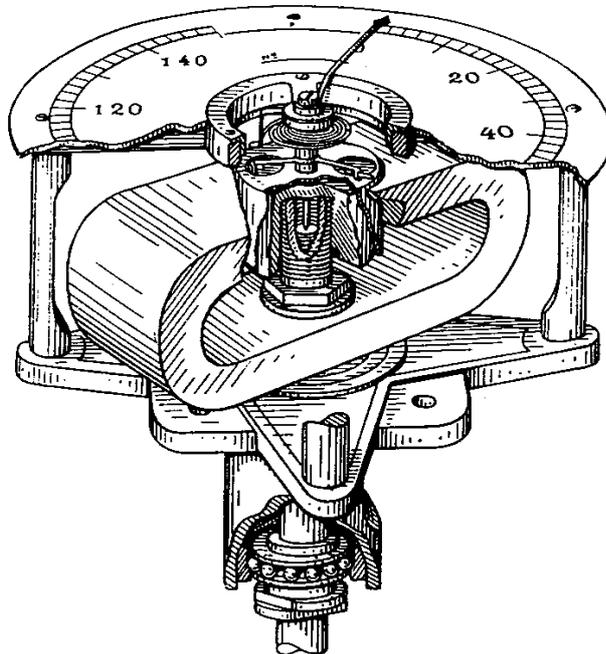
Schnitt durch einen Geschwindigkeitsmesser
